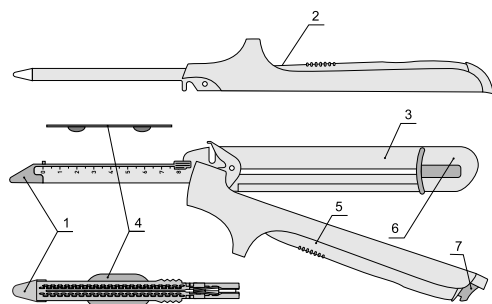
Внешний вид линейного сшивающе-режущего аппарата Volkman: 1 - сменная кассета; 2 - ответная часть корпуса; 3 - кассетная часть корпуса; 4 - предохранитель кассеты; 5 - ручка правого корпуса; 6 - ползунок ножа; 7 - кнопка открытия браншей.
